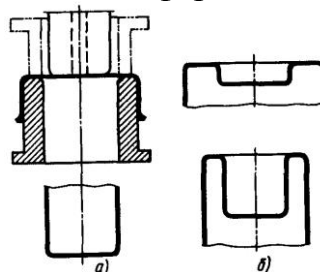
Реверсивная вытяжка: *а* — схема штампа; *б* — детали
